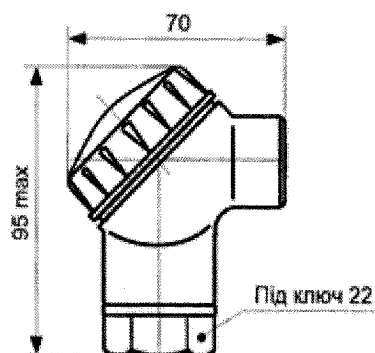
Кресленик зовнішньої частини ТХА-1090, ТХК-1090 з головкою типу ПБВИ.408724.003 СБ
